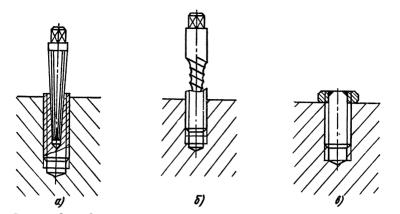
Способы удаления сломанных шпилек: a — зубчатым бором; b — коническим экстрактором с левой резьбой; b — с помощью приварной гайки
